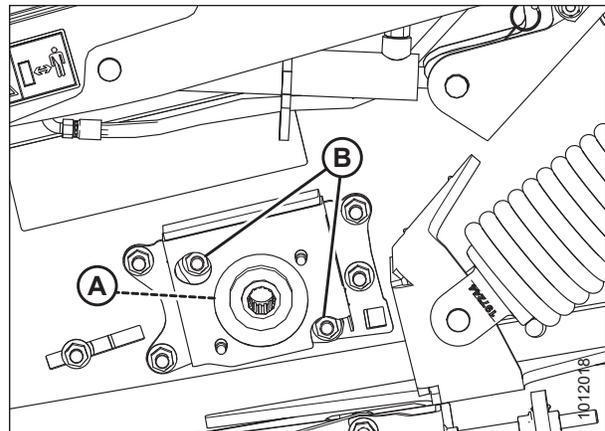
Rodillo de mando de la plataforma frontal izquierda
